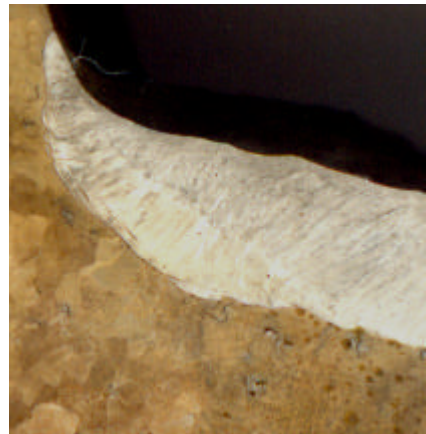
Makrostruktura vzorku 436.3 (zv. 1x)
